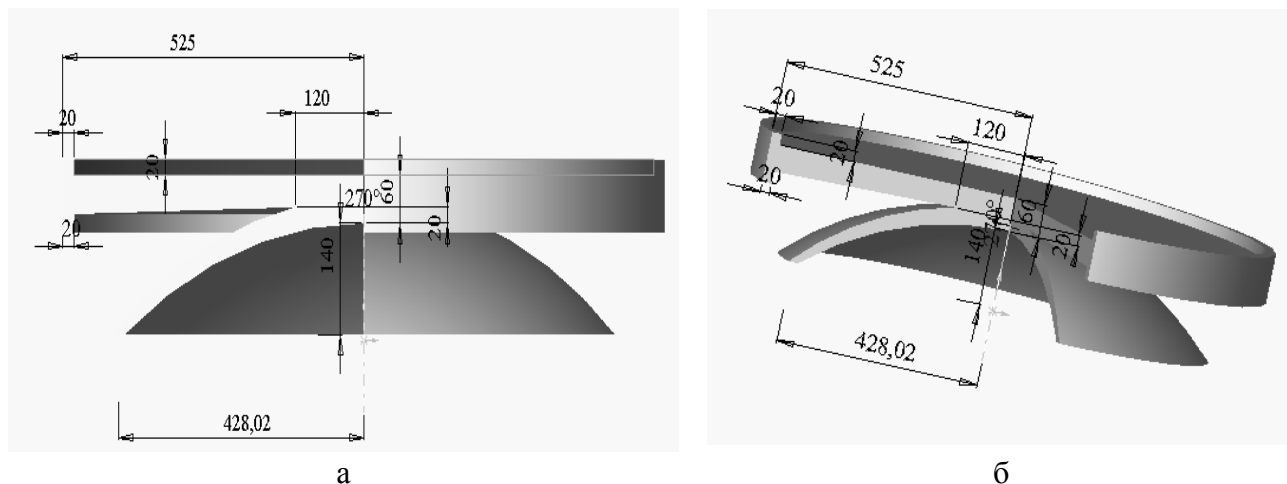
Чертеж клапана головки низкого давления: а – чертеж клапана; б – объемное изображение
